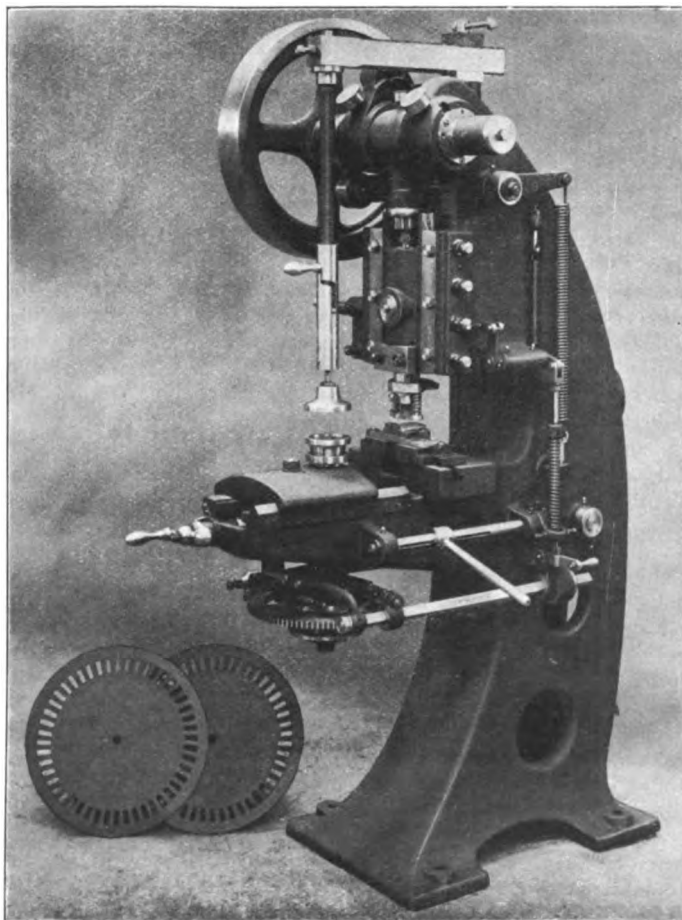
Nutenstanzmaschine mit elektromagnetischer Aufspannvorrichtung der Maschinenfabrik L. Schuler.
